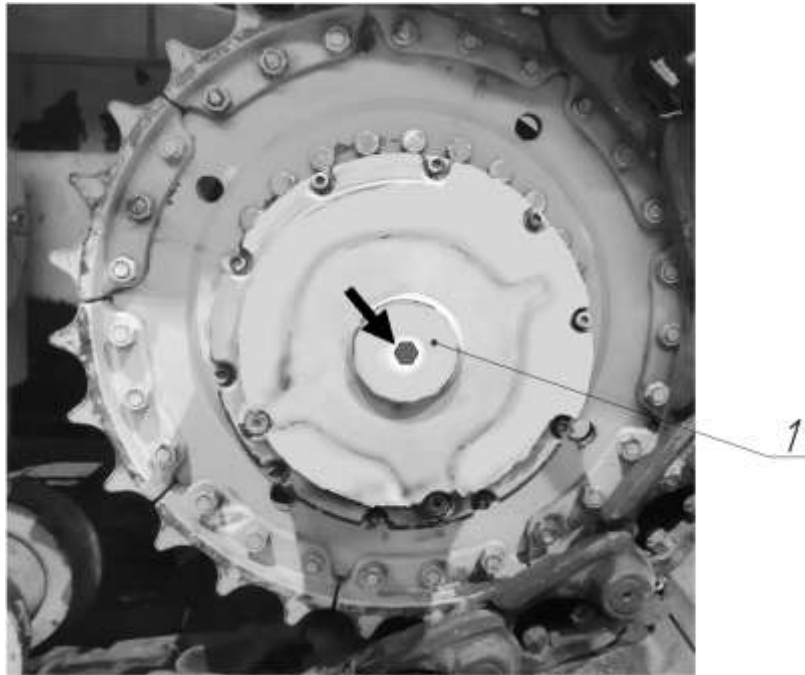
Крышка снятия вала для растормаживания редуктора
